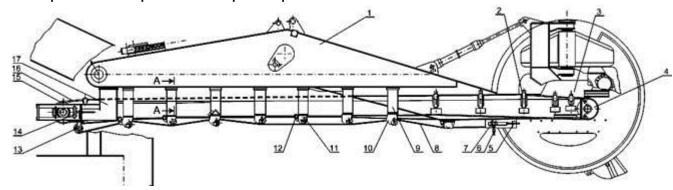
Основной и защитный конвейеры: 1 - стрела ротора; 2, 10 - роликоопоры; 3 - загрузочная воронка; 4, 7 - оборотные барабаны; 5, 14 - винтовые натяжные устройства; 6 - очиститель; 8, 16 - конвейерные ленты; 9 -
